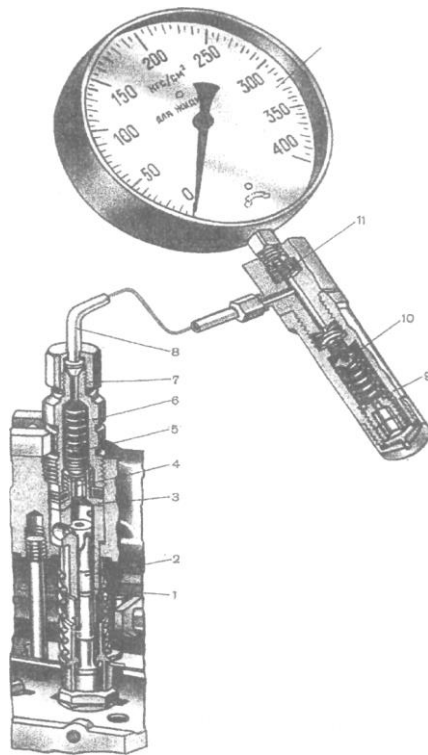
Пристрій КИ-4802 для перевірки прецизійних пар паливних насосів: 1 – втулка плунжера; 2 – плунжер; 3 – корпус клапана; 4 – клапан; 5 – пружина нагнітального клапана; 6 – штуцер насоса; 7 – гайка накидна; 8 – паливопровід високого тиску; 9 – пристрій КИ-4802; 10 – клапан запобіжний; 11 – демпфер; 12 – манометр; 13 – головка паливного насоса; 14 – секундомір.
